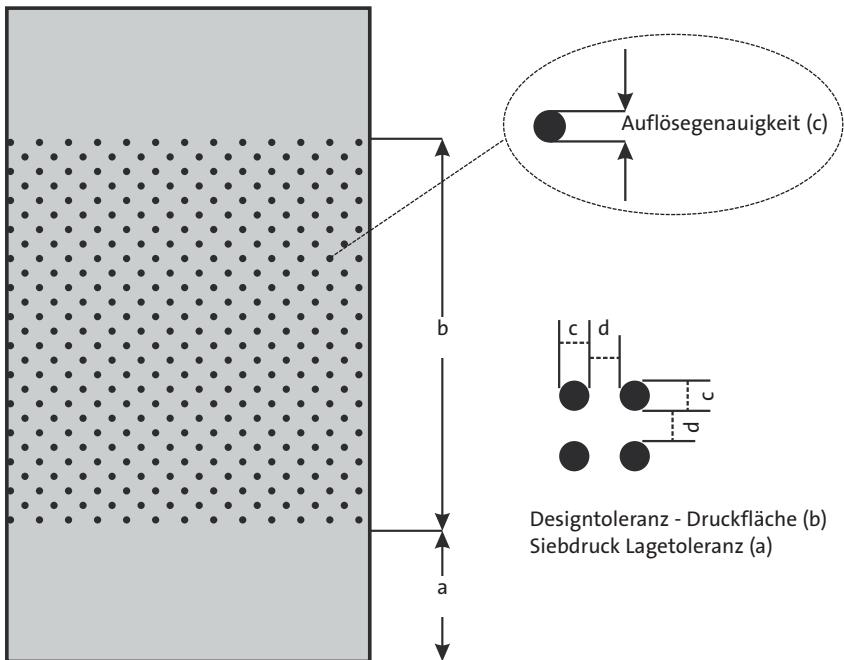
zu Tab. 22: Fehlerarten/Toleranzen für siebgedruckte Gläser
